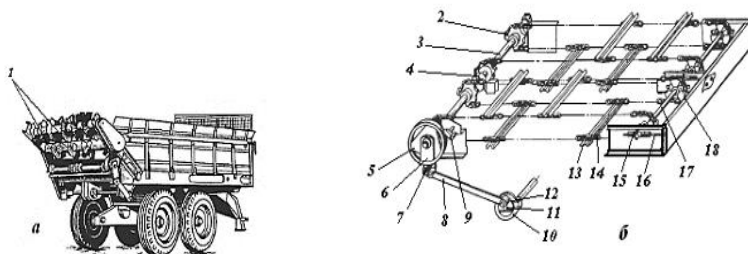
Розкидач органічних добрив РОУ-6: а - загальний вигляд; б - транспортер: 1 - розкидальний пристрій; 2 - ведуча зірочка; 3 - ведучий вал; 4 - опорний підшипник; 5 - храпове колесо; 6 - щоби; 7 - ведуча собачка; 8 - тяга; 9 - запобіжна собачка; 10 - корпус кривошипа; 11 - куліса; 12 - диск кривошипа; 13 - скребок; 14 - ланцюг; 15 - гайка; 16 - натяжний болт; 17 - ведений вал; 18 - ролик
